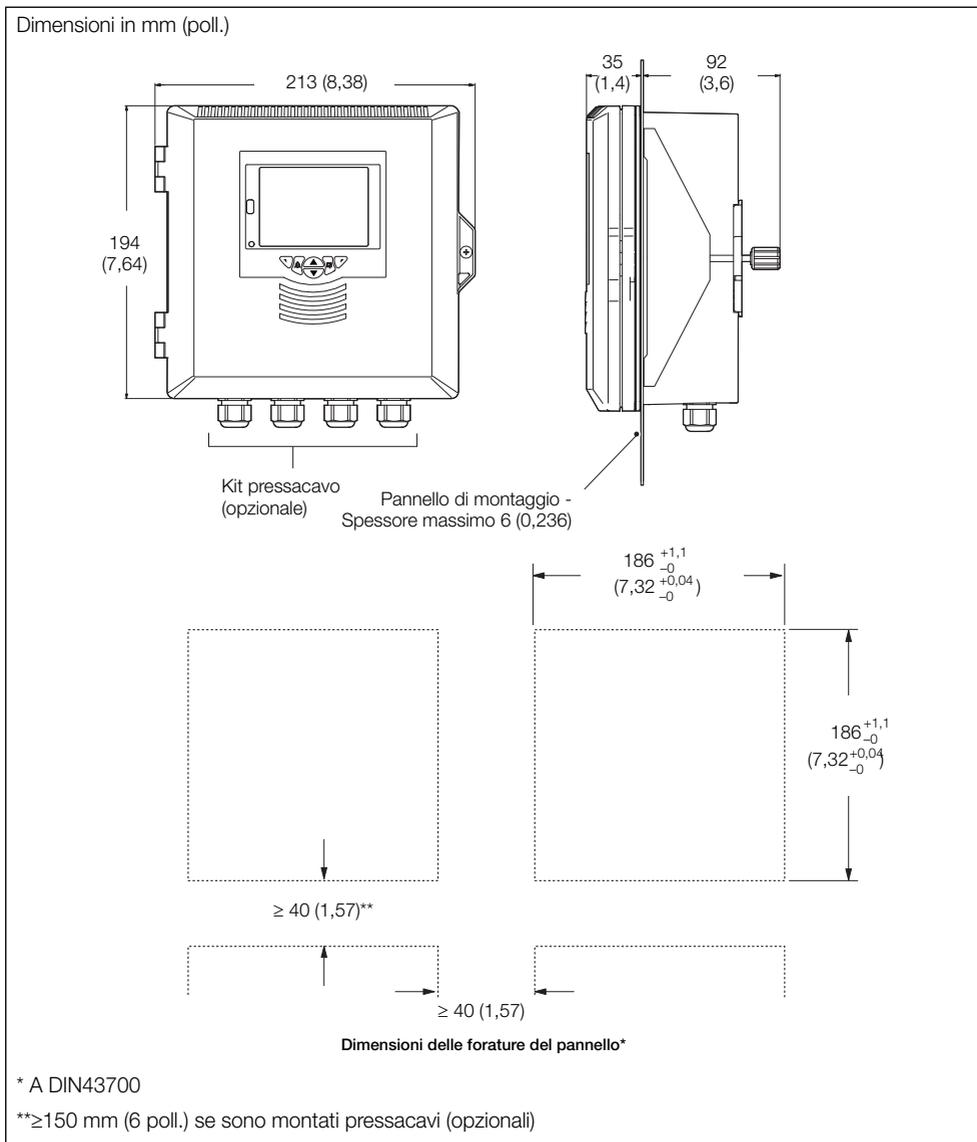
ControlMaster CMF310 per montaggio su pannello
